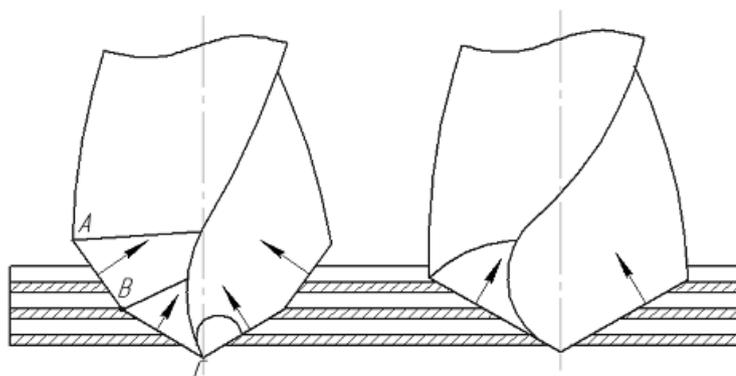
Схема движения стружки а) СДЗ тип 1, б) стандартное сверло
